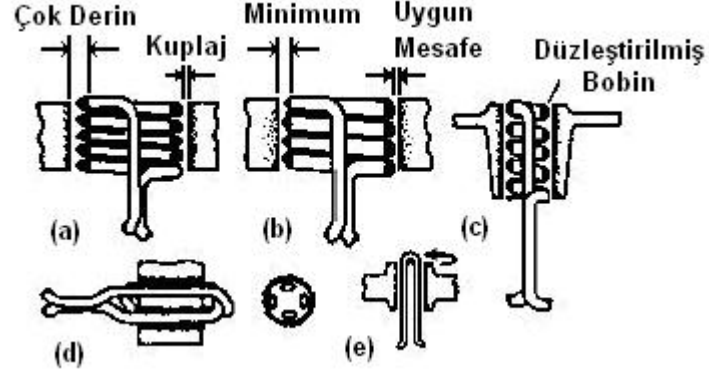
Bölgesel ısıtma için değişik şekilli bobinler
